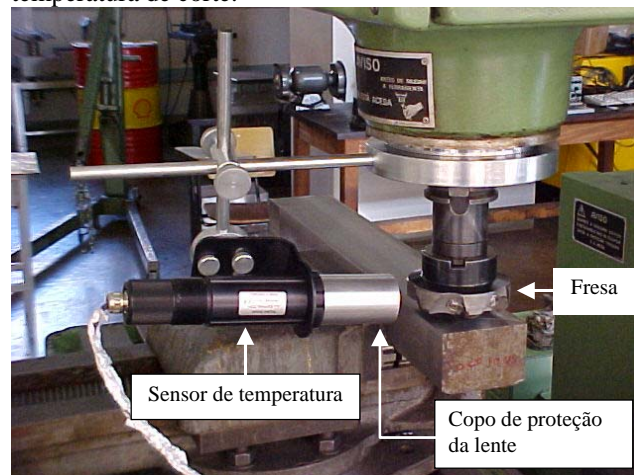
Dispositivo de fixação com o sensor de temperatura montado na fresadora.
